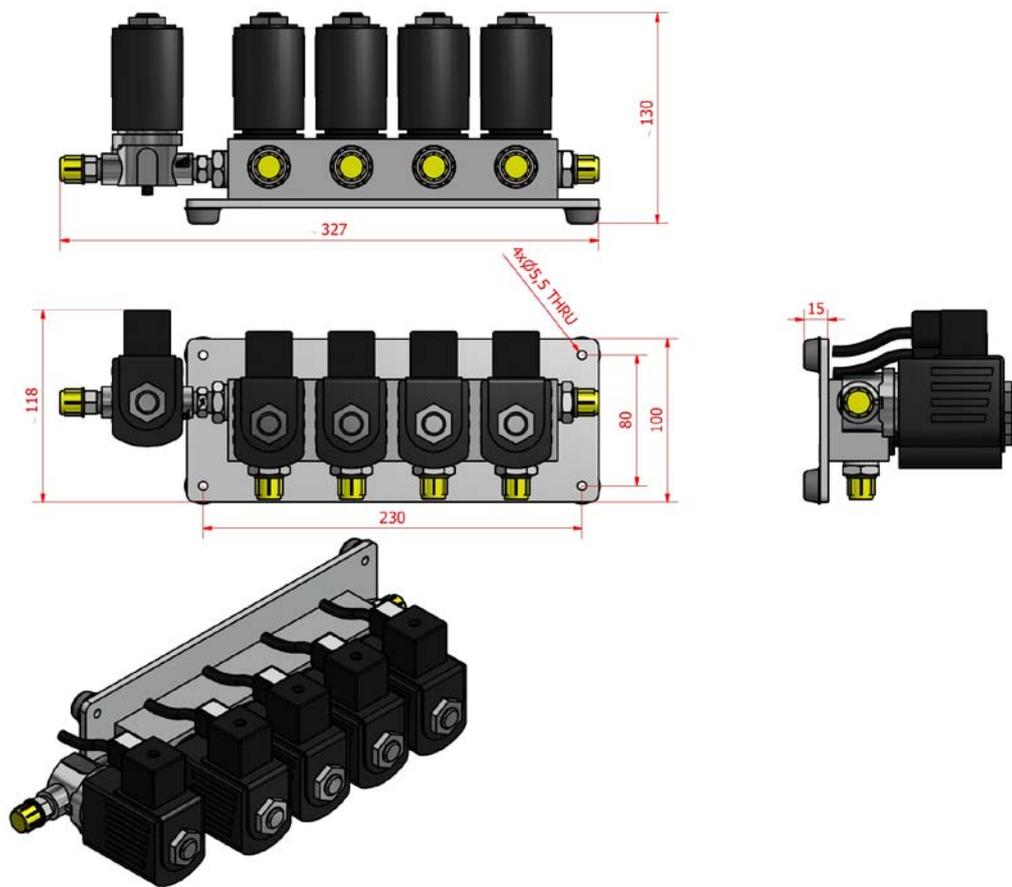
Dimensions du bloc de vannes 4+1 INDUCT (en mm)
